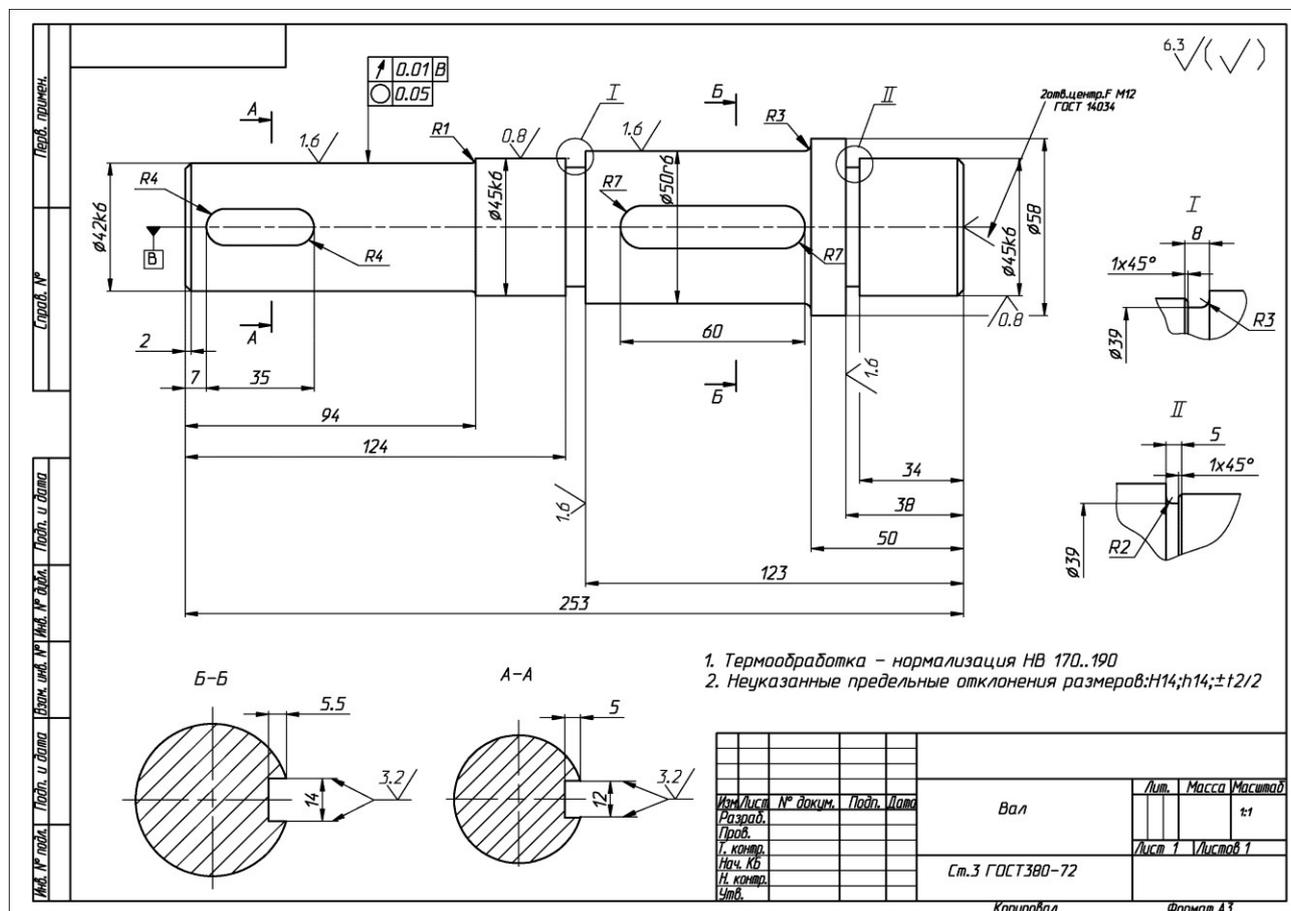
Пример выполнения рабочего чертежа вала редуктора
